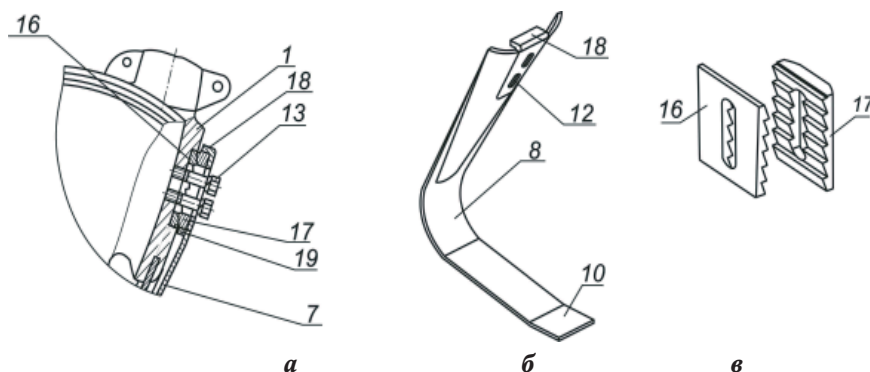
Прижимная пластина и упорные накладки: а – в сборе; б – пластина, в – упорные накладки
